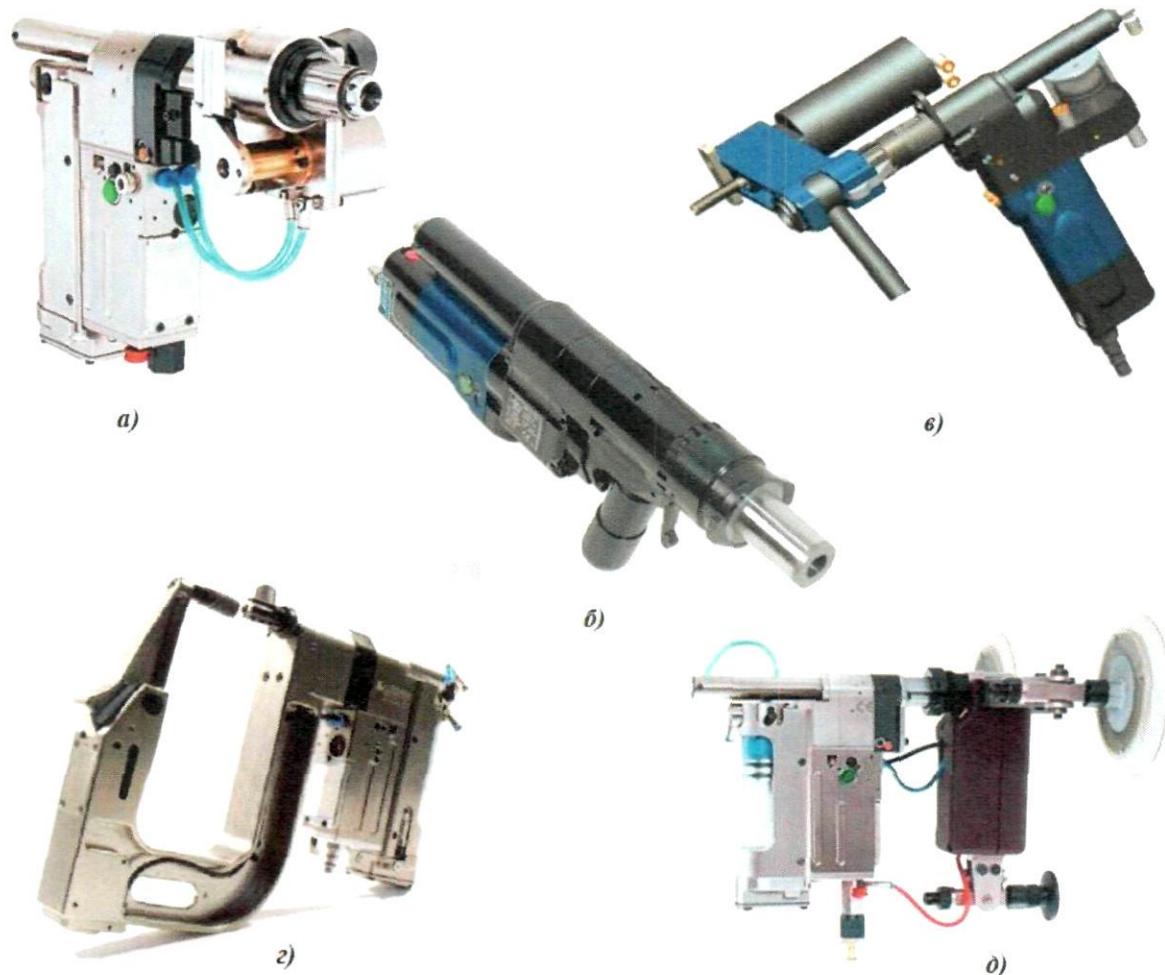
Сверлильные машины с автоматической подачей (СМАП)
